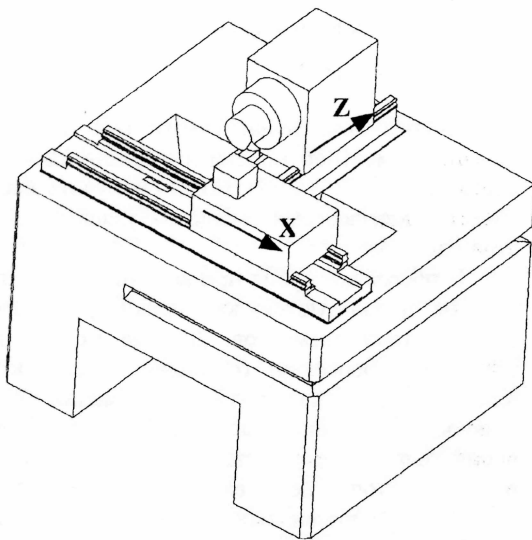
Расположение основных узлов для рассматриваемой компоновки токарного станка с двумя суппортами
